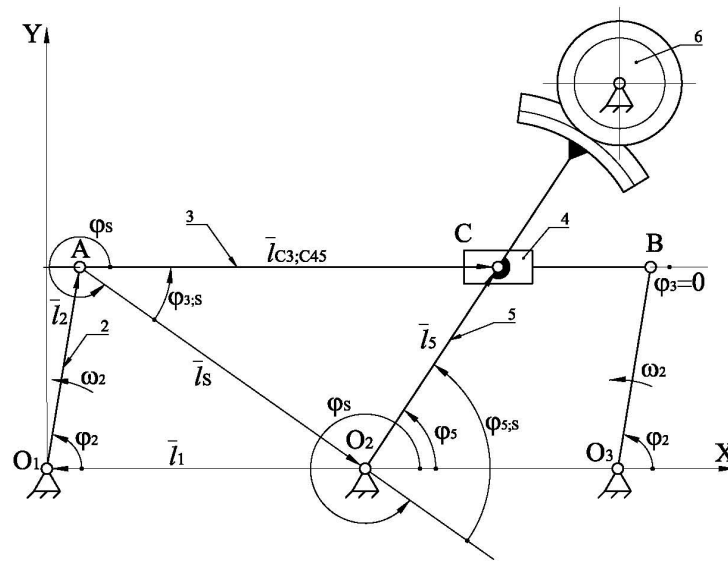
Розрахункова схема кулісного механізму реверсного руху круглопанчішного автомату:
